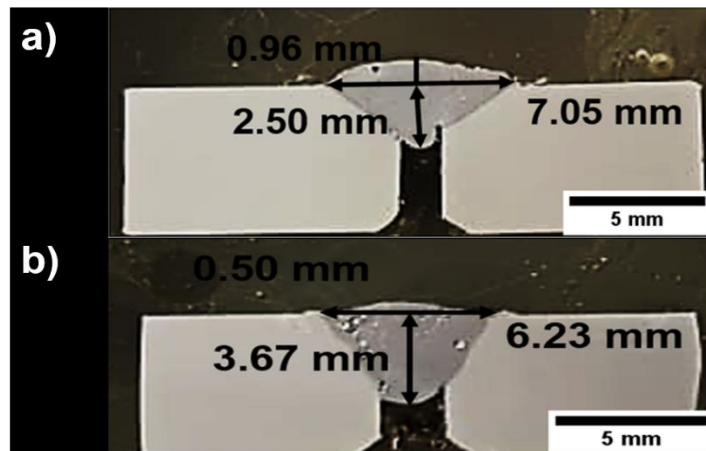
91 Unión de las placas de aleación de aluminio a) Soldadura 4 y b) réplica de la soldadura 4.
